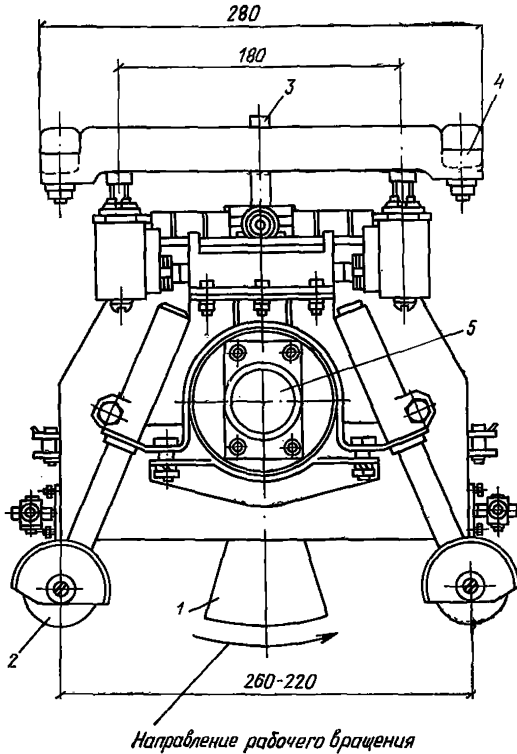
Инструмент для вскрытия стыков (стыкорез) конструкции ПКБ ЛНИИ АКХ
